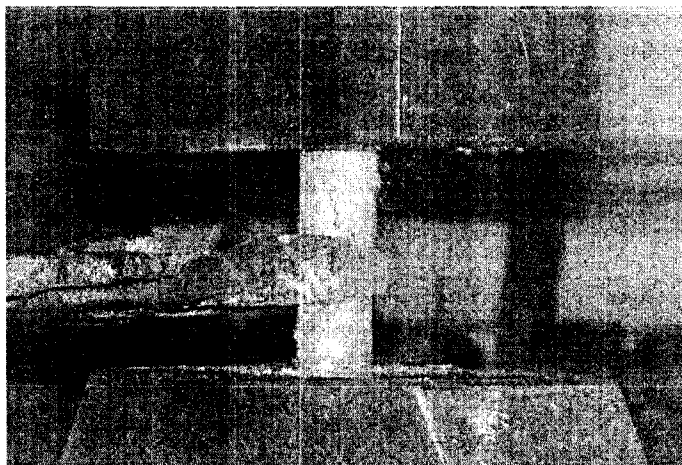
Всесторонняяковка заготовки пневматическим молотом
